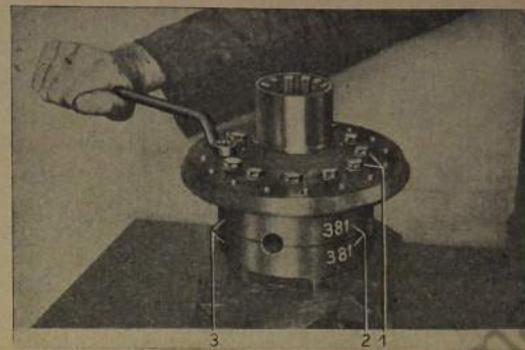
Ausgleichgehäusehälften auseinanderschrauben
